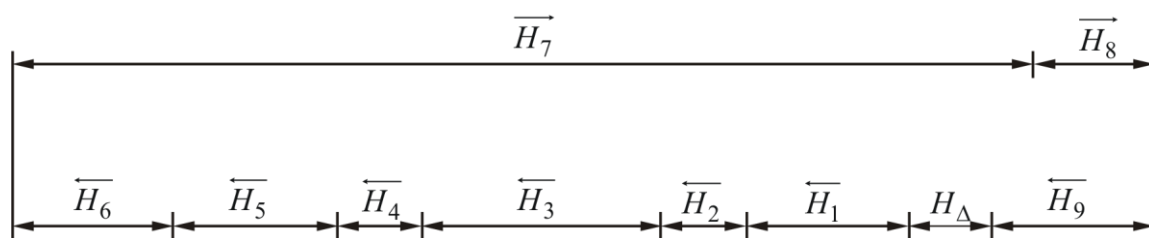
Схема сборочной размерной цепи вала зубчатого колеса
